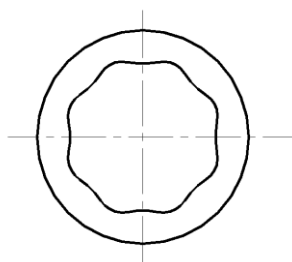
Форма внутренней поверхности трубы после редуцирования на стане с двухвалковыми рабочими клетями.
